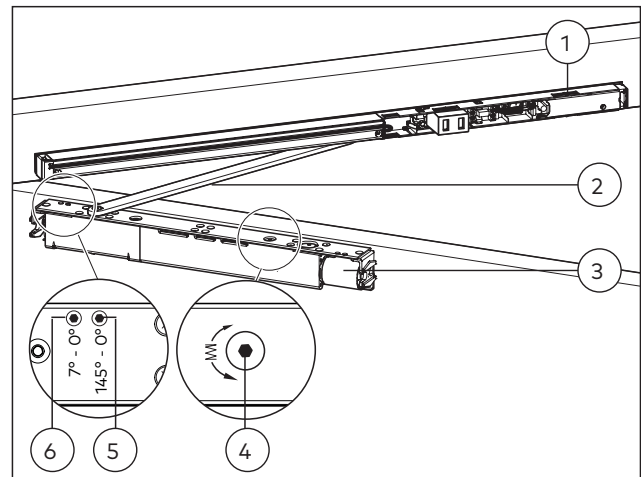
Vue d'ensemble du TS 97 FLR-K XEA
